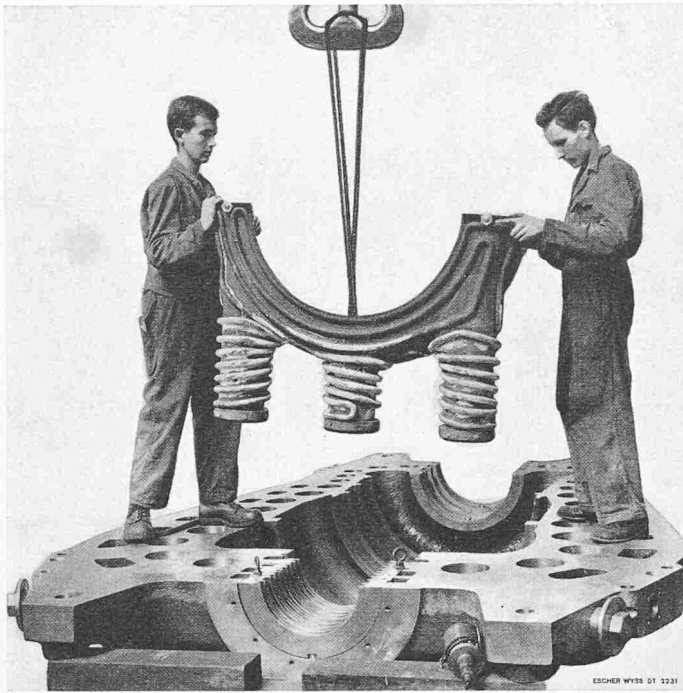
Kühlschild mit aufgeschweissten Rohren beim Einbau in das Hochdruck-Gehäuse
